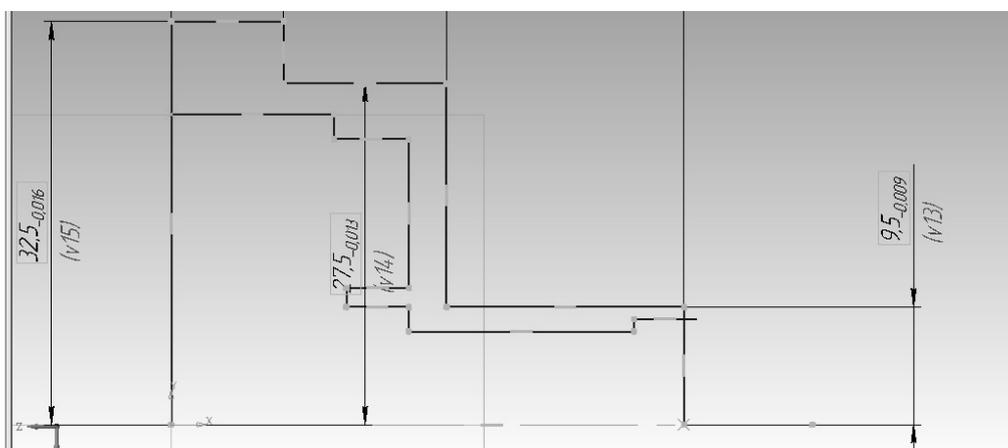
Внутренний контур детали, проведенный «на глаз»
